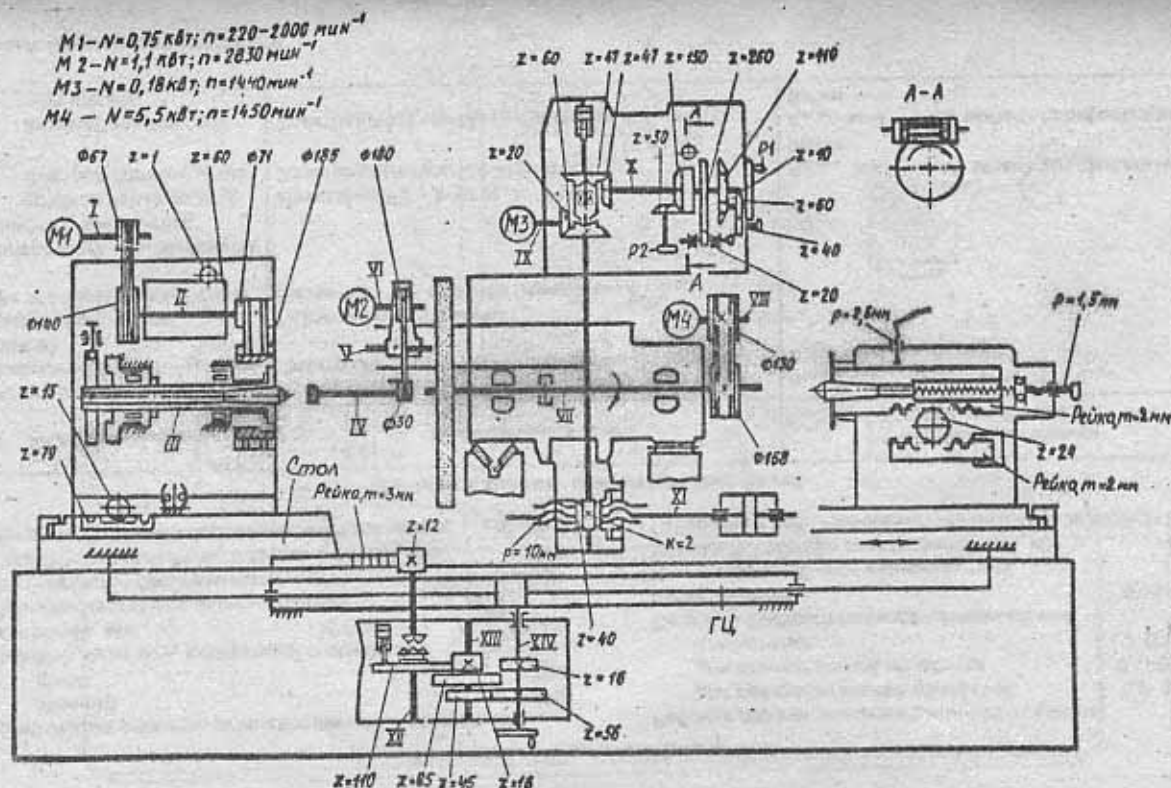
Кинематическая схема круглошлифовального станка мод. ЗУ131
